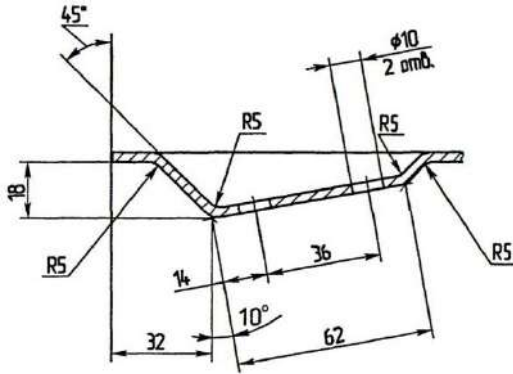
Фрагмент креслення кузовної деталі
